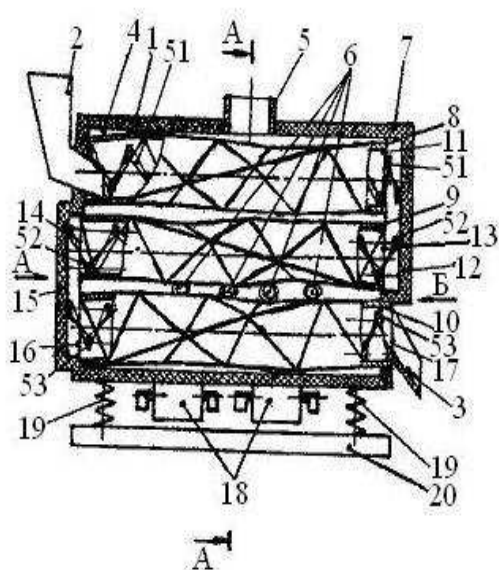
Установка для непрерывной сушки сыпучих материалов, вид спереди
